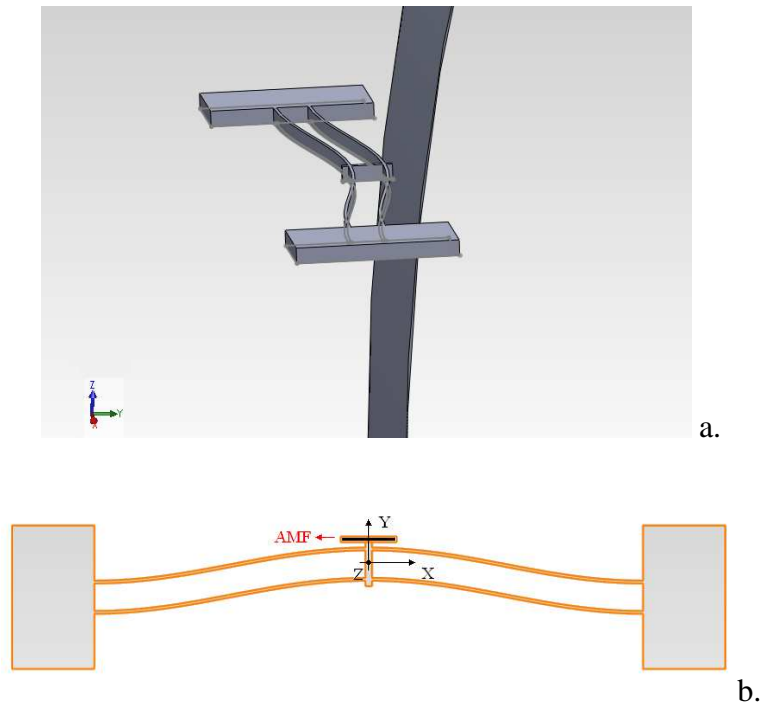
poutre double pré-formée au contact avec une languette d'AMF
